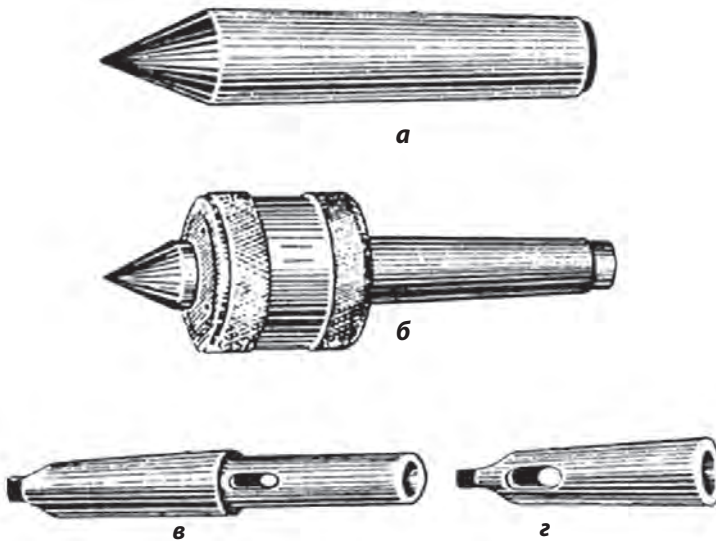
Деталі з конічними поверхнями: а, б – токарні центри; в, г – перехідні втулки
